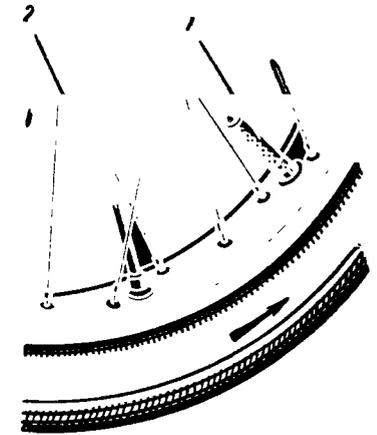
Установка барашка для предохранения от проветывания шины: 1—вентиль; 2—барашек.
